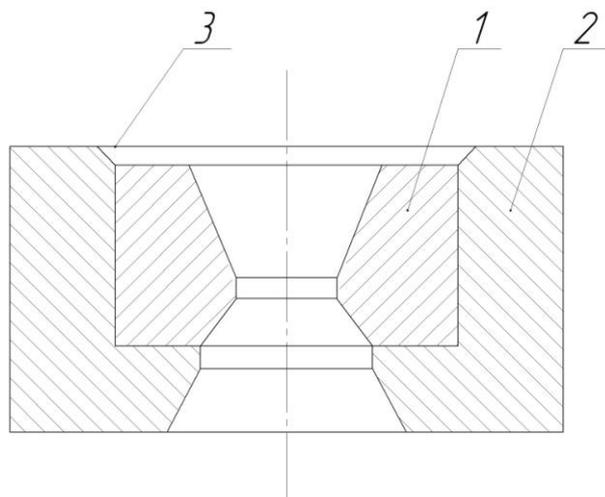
Запайка заготовки: 1—заготовка; 2—оправки; 3—место запайки.
